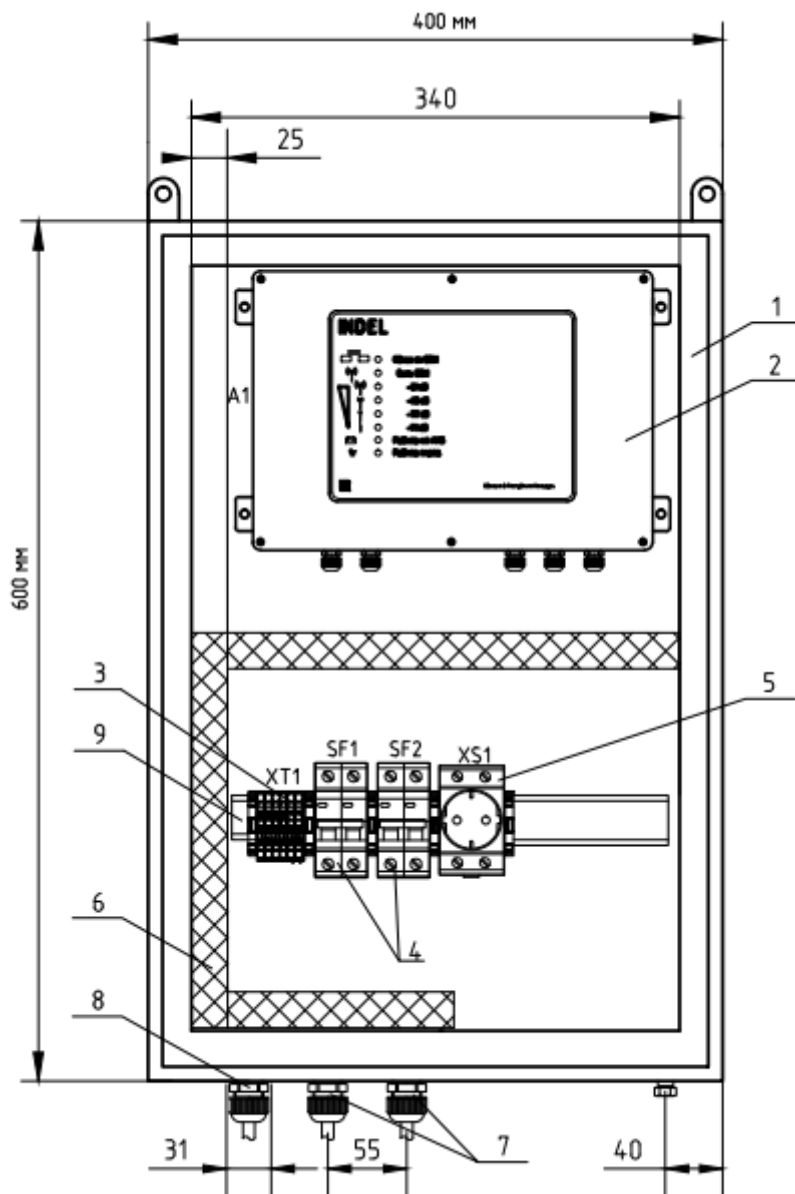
Общий вид (внутренний) и габаритные размеры ШУТЭ.
